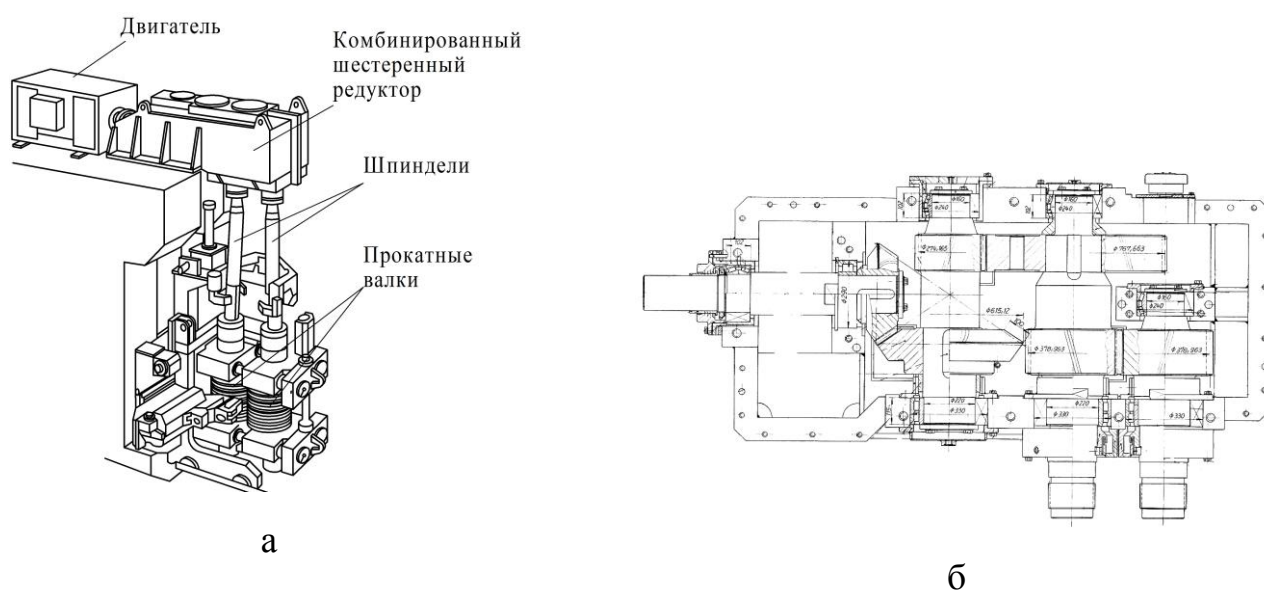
Общий вид прокатной клетки сортового стана (а) и разрез комбинированного редуктора привода (б)
